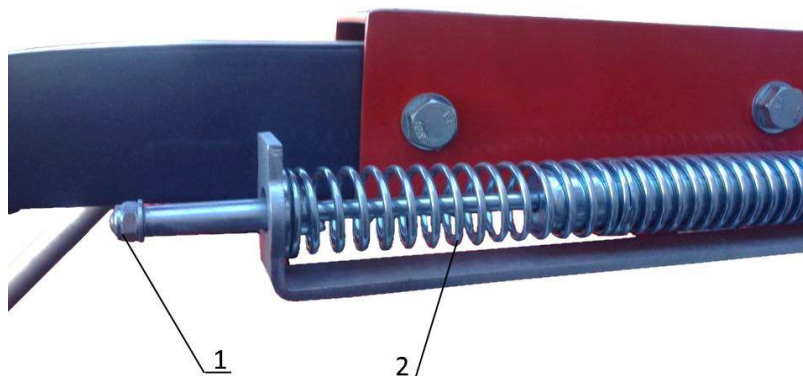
Регулировка натяжения пружины предохранительного рычага:
